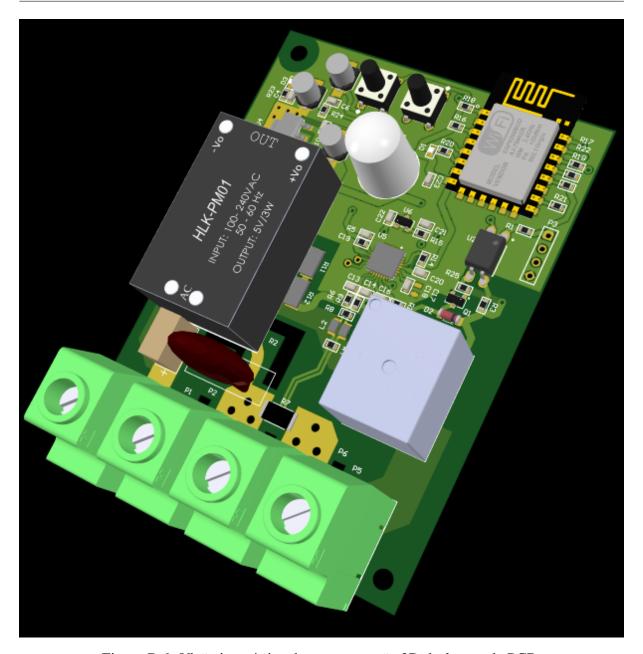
Visão isométrica da representação 3D do *layout* da PCB.
